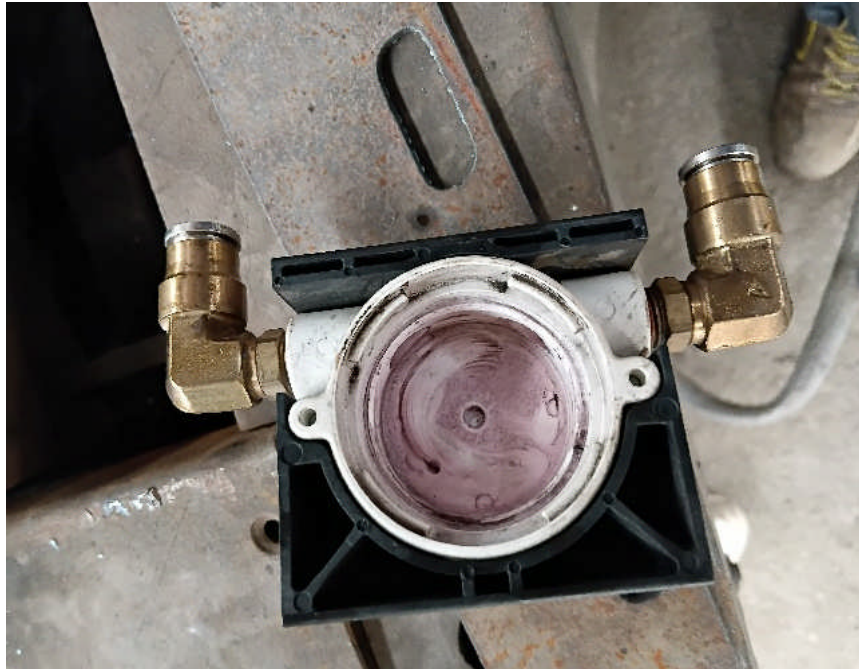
Capteur de pression à turbine – Vue interne après démontage et inspection
